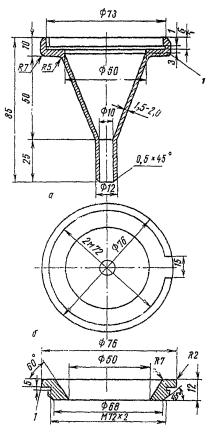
Аллонж открытый (патрон для фильтра): a — корпус; δ — гайка; I — накатка
